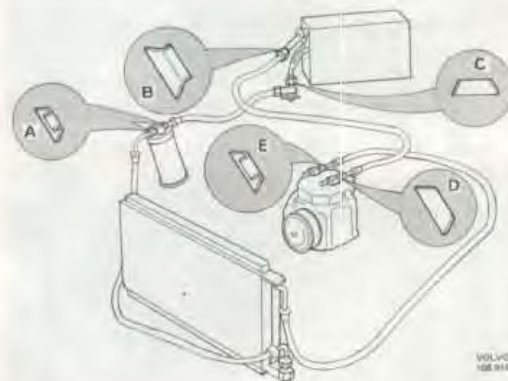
Placering av kopparbrickor i anläggning sen. utf.
